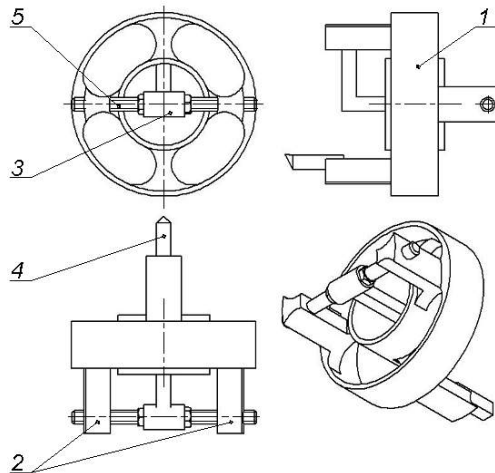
Конструкция устройства измеряющего и стабилизирующего усилия резания: (1 – тензорезисторный датчик силы; 2 – дополнительная пара силовводящих рычагов; 3 – бесконтактный сельсин; 4 – резец; 5 – вал ротора)
